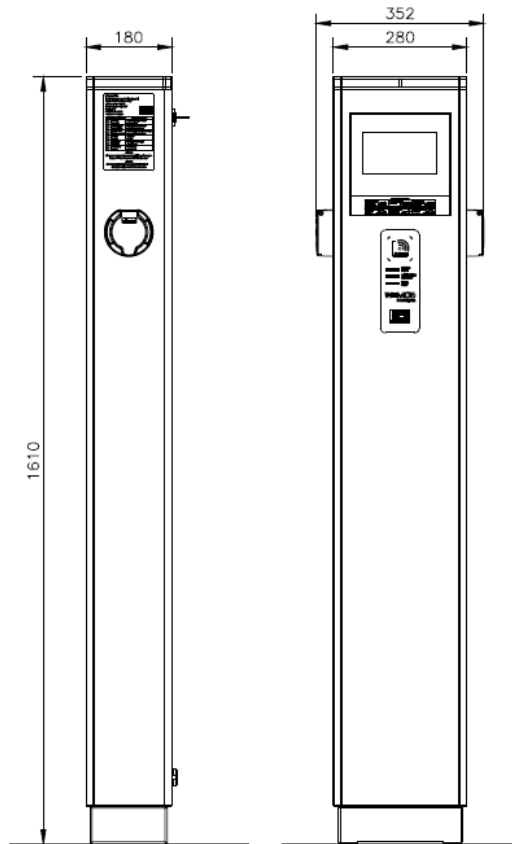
Dimensional da WEMOB-P-022-E-3G-R-H-2S2
